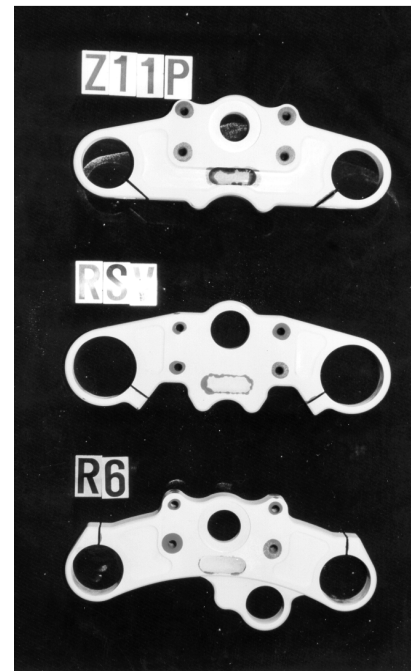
Rissanalyse der ABM-Gabelbrücken A, D, E.
